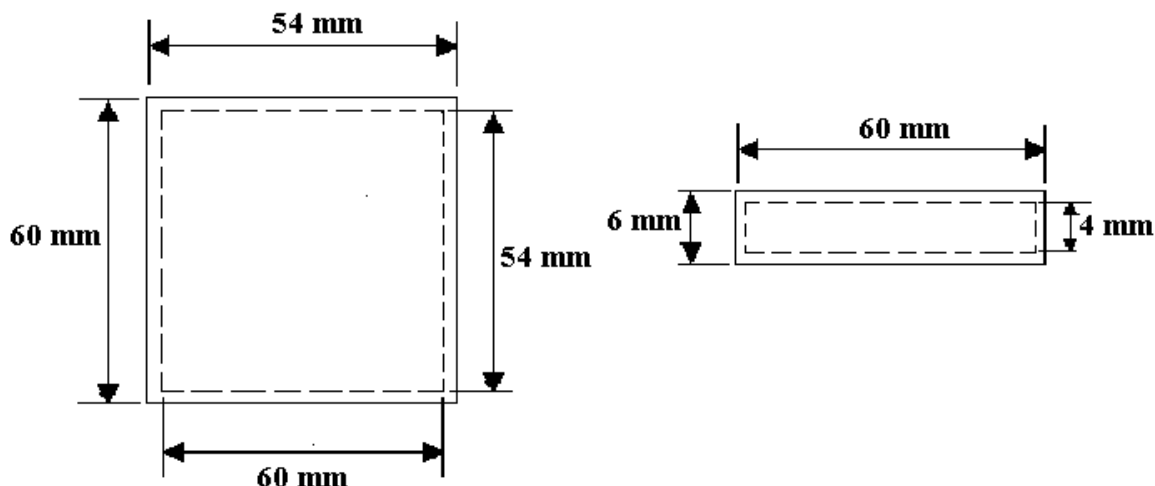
Dimensões do tubo de calor retangular construído.
